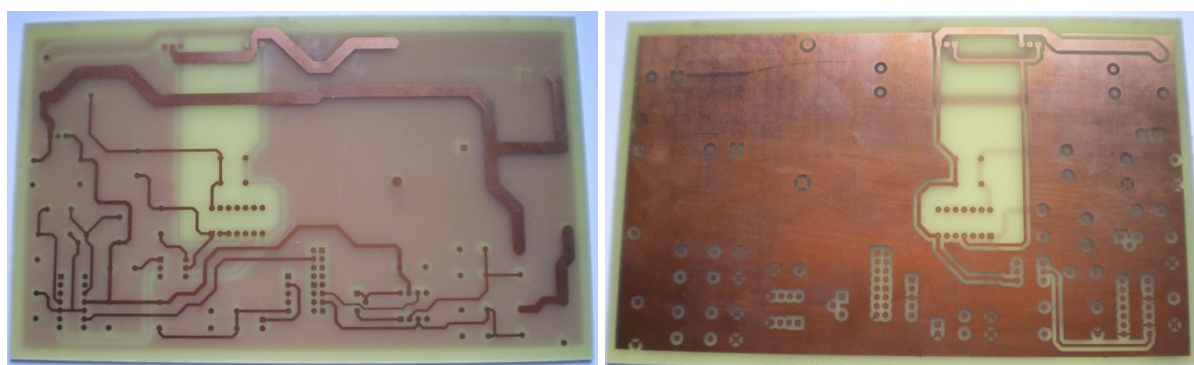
Imágenes del diseño de pistas (izquierda) y plano de masa (derecha) de la placa.
